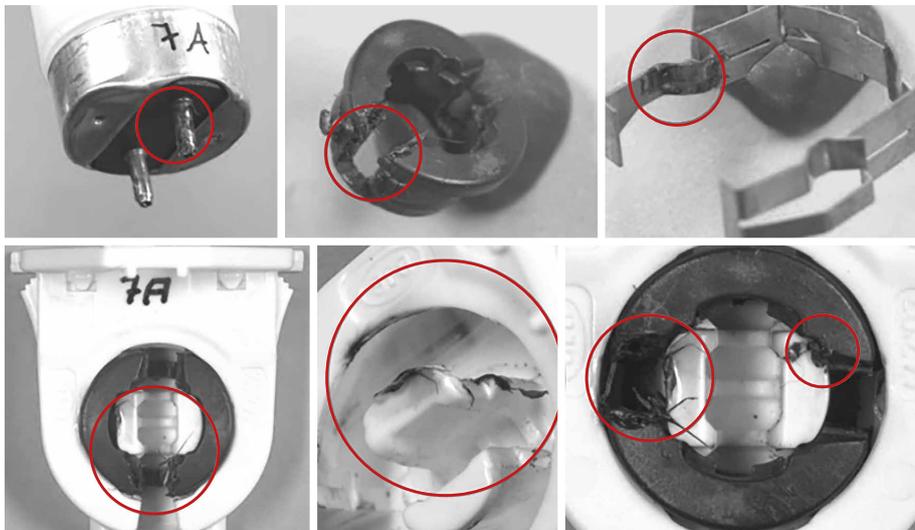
Beschädigte Fassungen, in denen Retrofit-Lampen mit zu hohem Gewicht betrieben wurden
